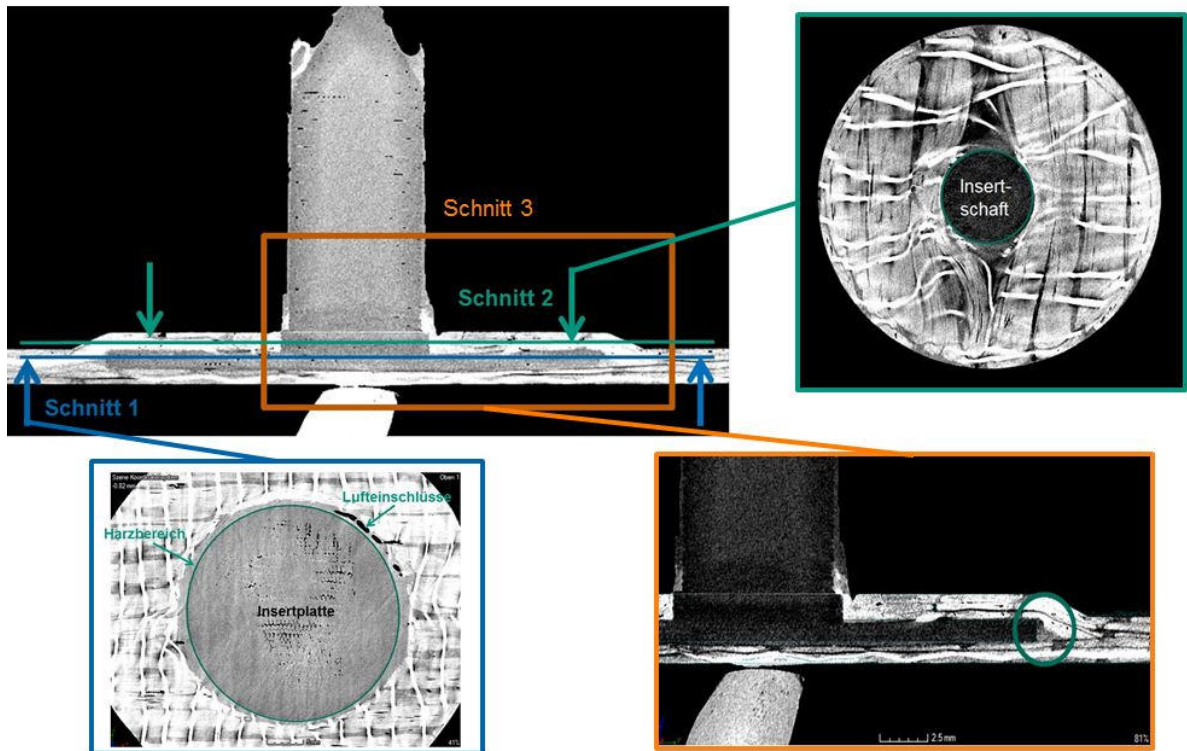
CT-Aufnahmen einer CFK-Platte mit integriertem Insert
